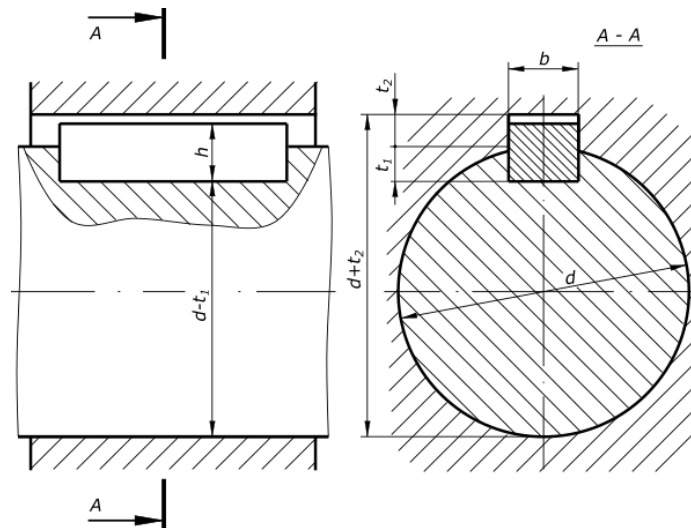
Розрахункова схема з'єднання призматичною шпонкою.
